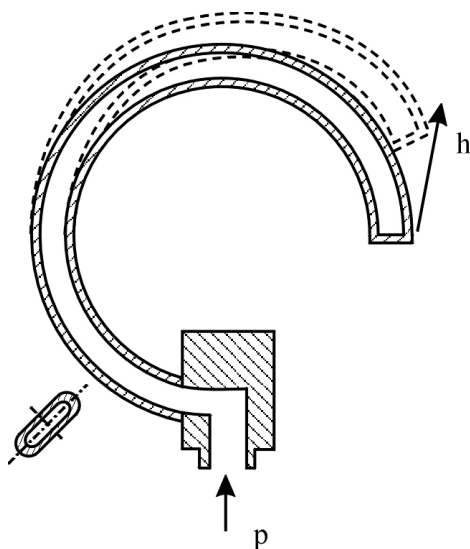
Пружний чутливий елемент – трубчаста пружина
